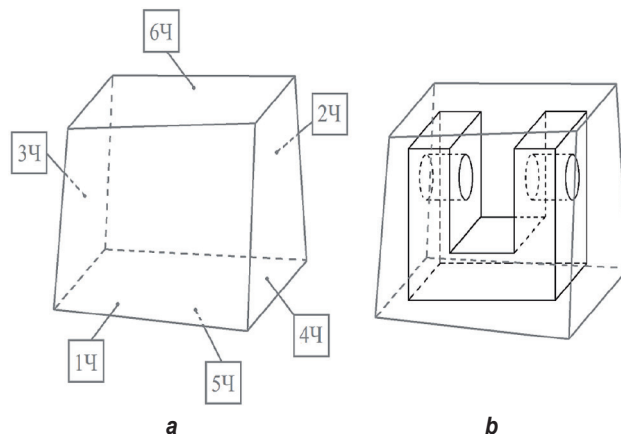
Заготовка с обозначенными поверхностями (а) и деталь, вписанная в заготовку (b)
